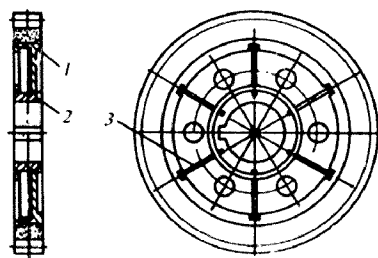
Зубчатый шевер для работы с окружным нагружением на станках с синхронным приводом инструмента и детали:
